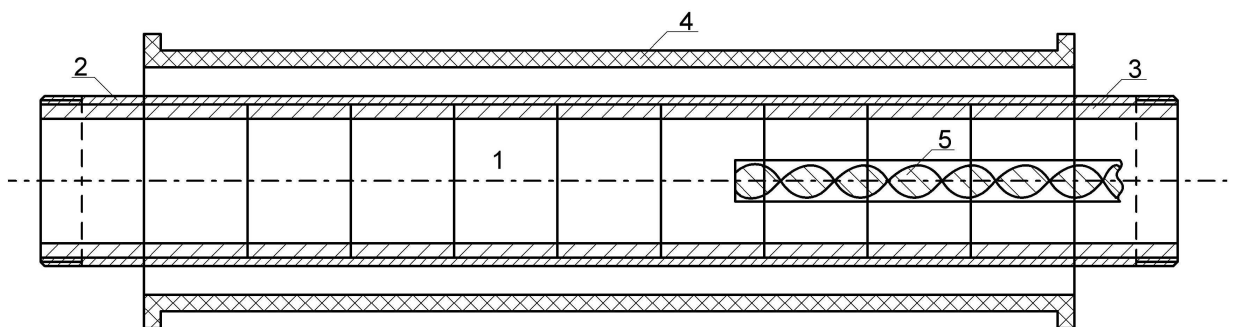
Продольный разрез новой конструкции реакционной камеры для получения нитрида алюминия газофазным способом:
